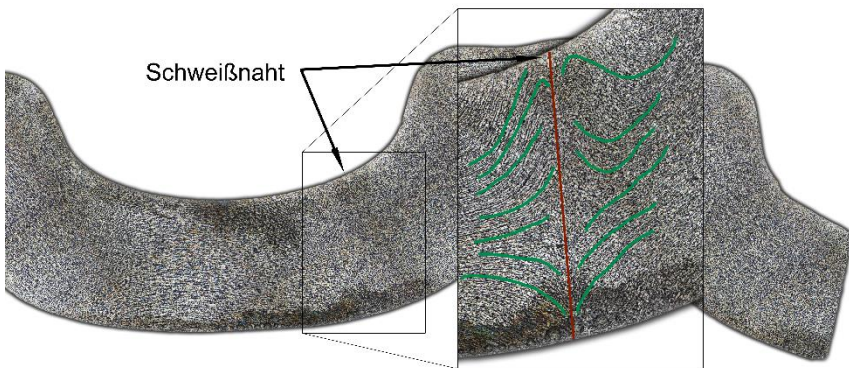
Schliffbild des Profils an der Schweißnaht.
